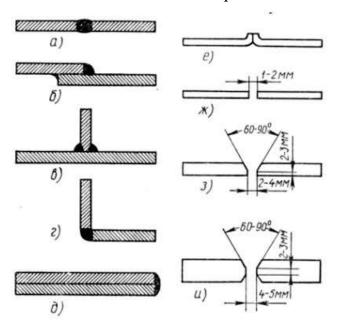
Типы сварных соединений и подготовка кромок сварного шва: а — стыковое; б — внахлестку; в — тавровое; г — угловое; д — боковое; е, ж, з, и — подготовка кромок
